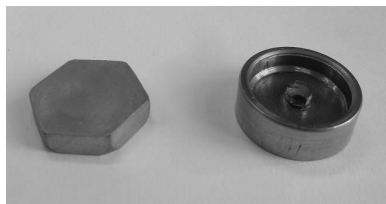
Заготовка шестигранник $h=5.5$ мм.
